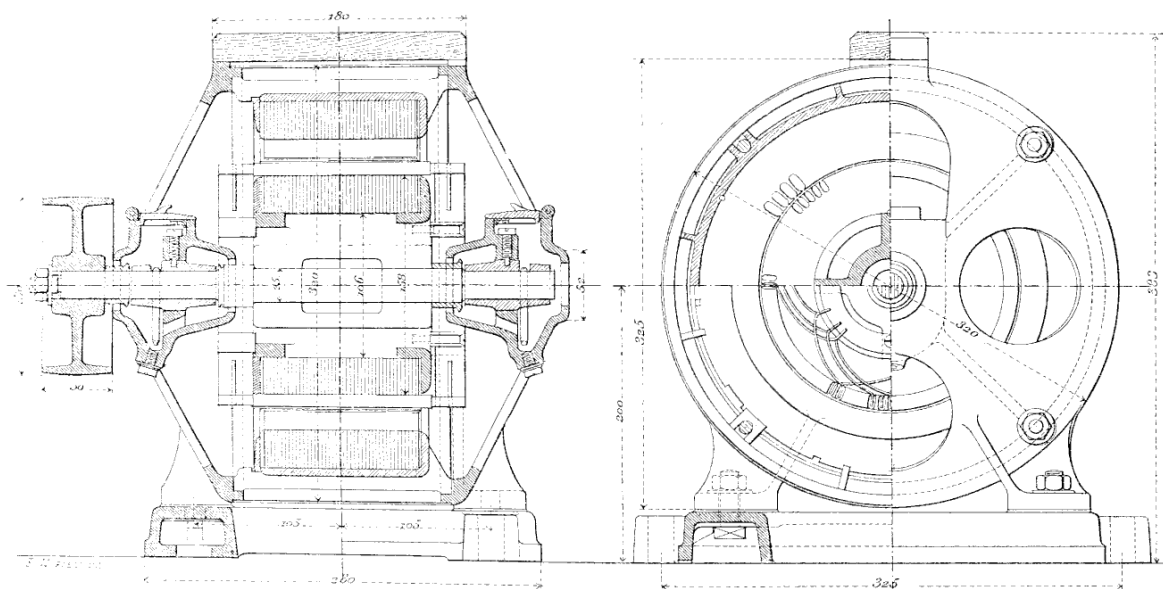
Coupe longitudinale. — FIG. 45. — Vue par bout avec coupe transversale partielle.
